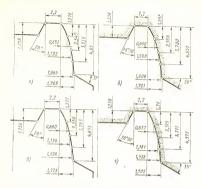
Проекция режущей кромки на плоскость контроля и профиль шлифовального круга фрез для обработки шлицевых валиков: а и 6—для фрез с винтовыми канавками; а и г—для фрез с прямыми канавками
